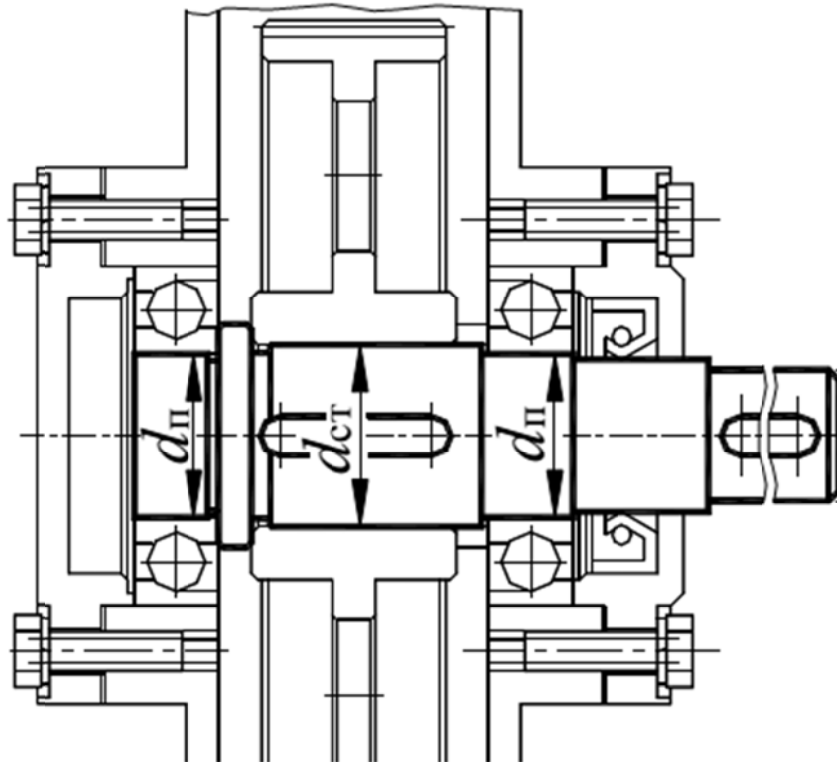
Шпоночное соединение ступицы цилиндрического колеса с валом
